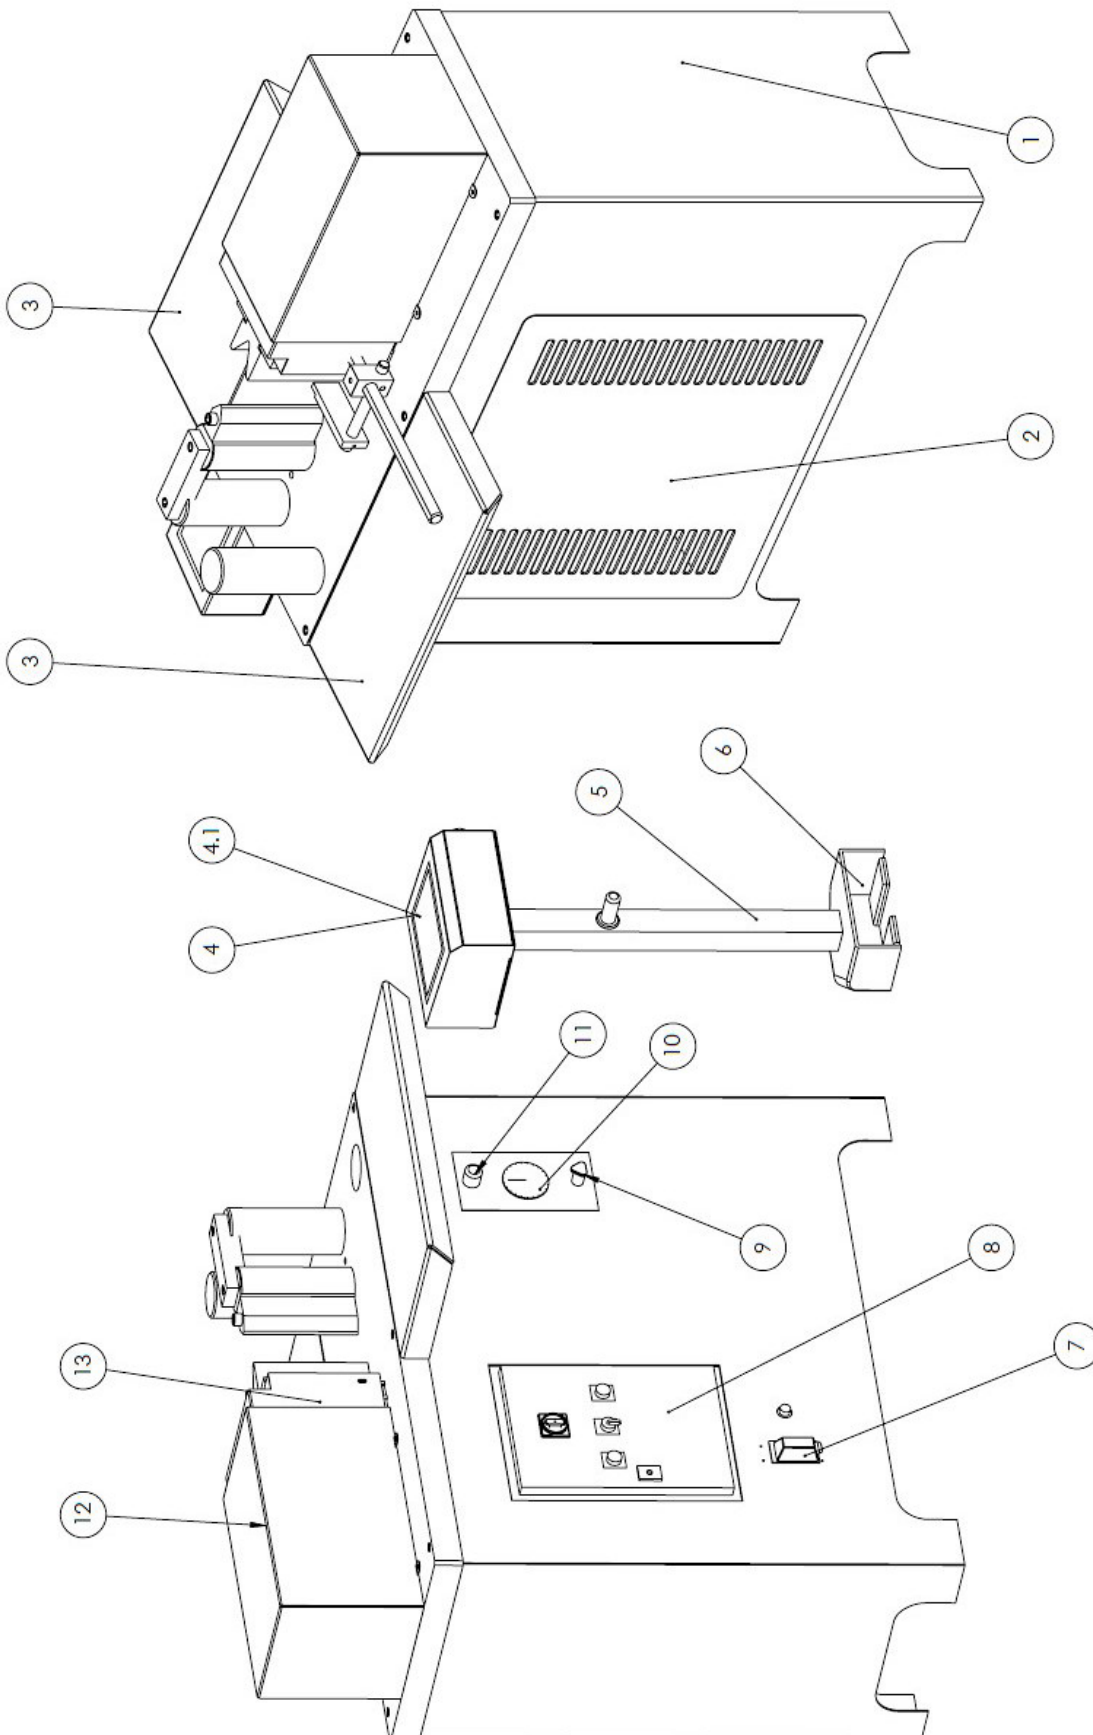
Ersatzteilzeichnung 1 Gesamtmaschine HBP 20
